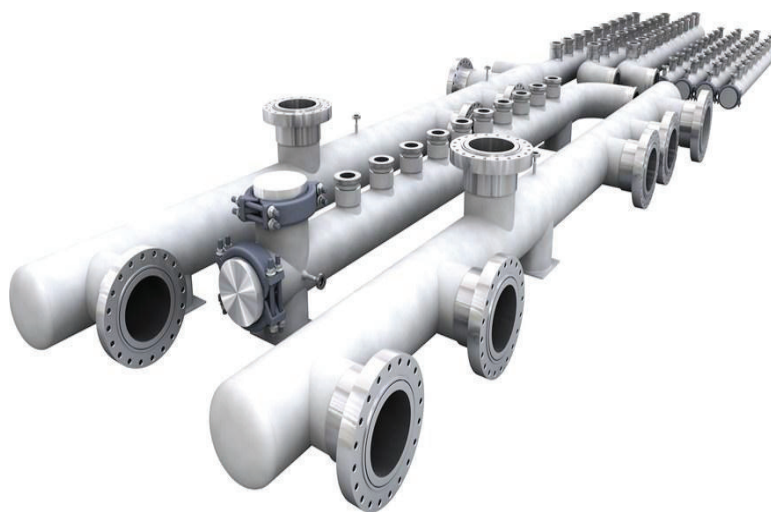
Intercambiador de calor de carcasa y tubo
